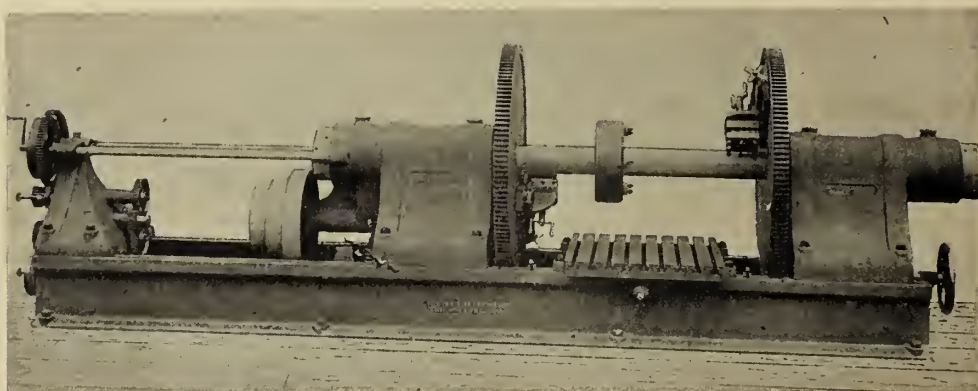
Machine à aléser les cylindres de locomotives type *Sellers*.
